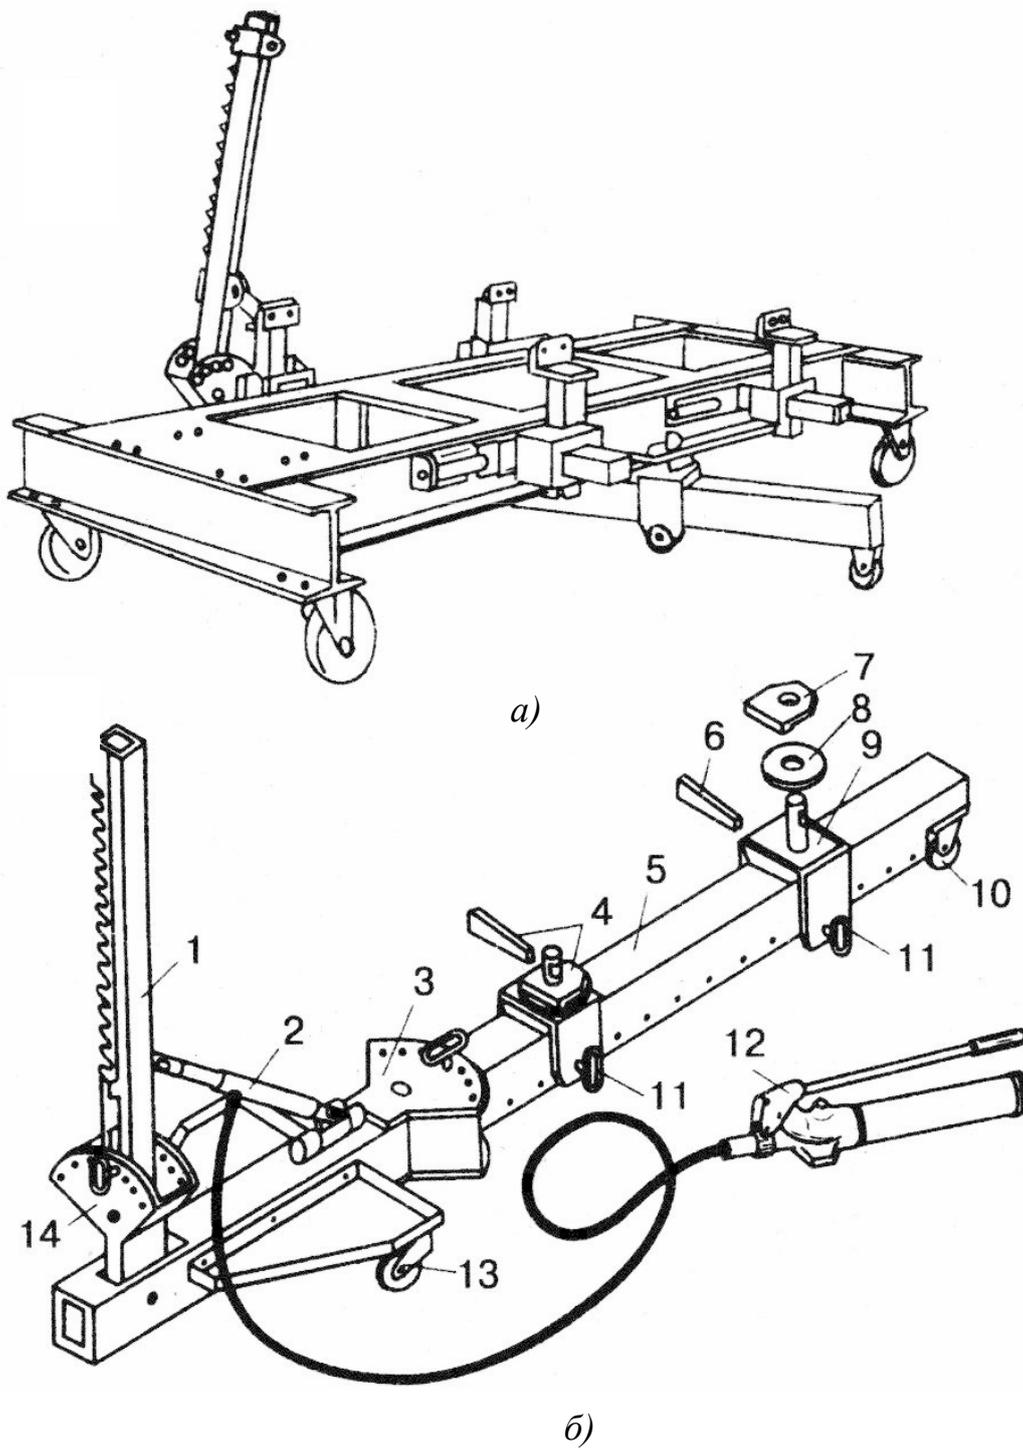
Установка БС-124: а – вариант закрепления устройства на установке БС-124; б – общий вид установки; 1 – силовой рычаг; 2 – силовой гидроцилиндр; 3 – поворотная балка; 4 – зажимное приспособление; 5 – основная балка; 6 – клин; 7, 8 – зажимные шайбы; 9 – подвижное зажимное приспособление; 10 – неповоротное колесо; 11 – стопор; 12 – гидравлический насос; 13 – поворотные колеса; 14 – серьга
